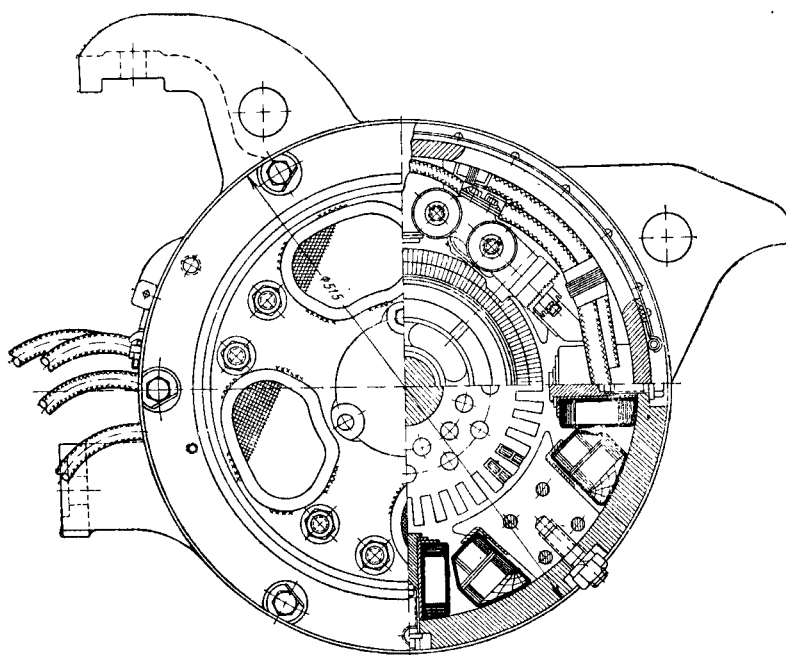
Габаритные размеры двигателя типа ДК-104Г
